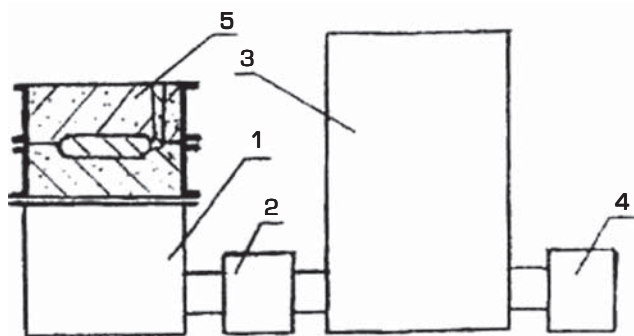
Схема установки вакуумного прошивания: 1 – приемный стол; 2 – клапан; 3 – ресивер; 4 – вакуумный насос; 5 – форма
